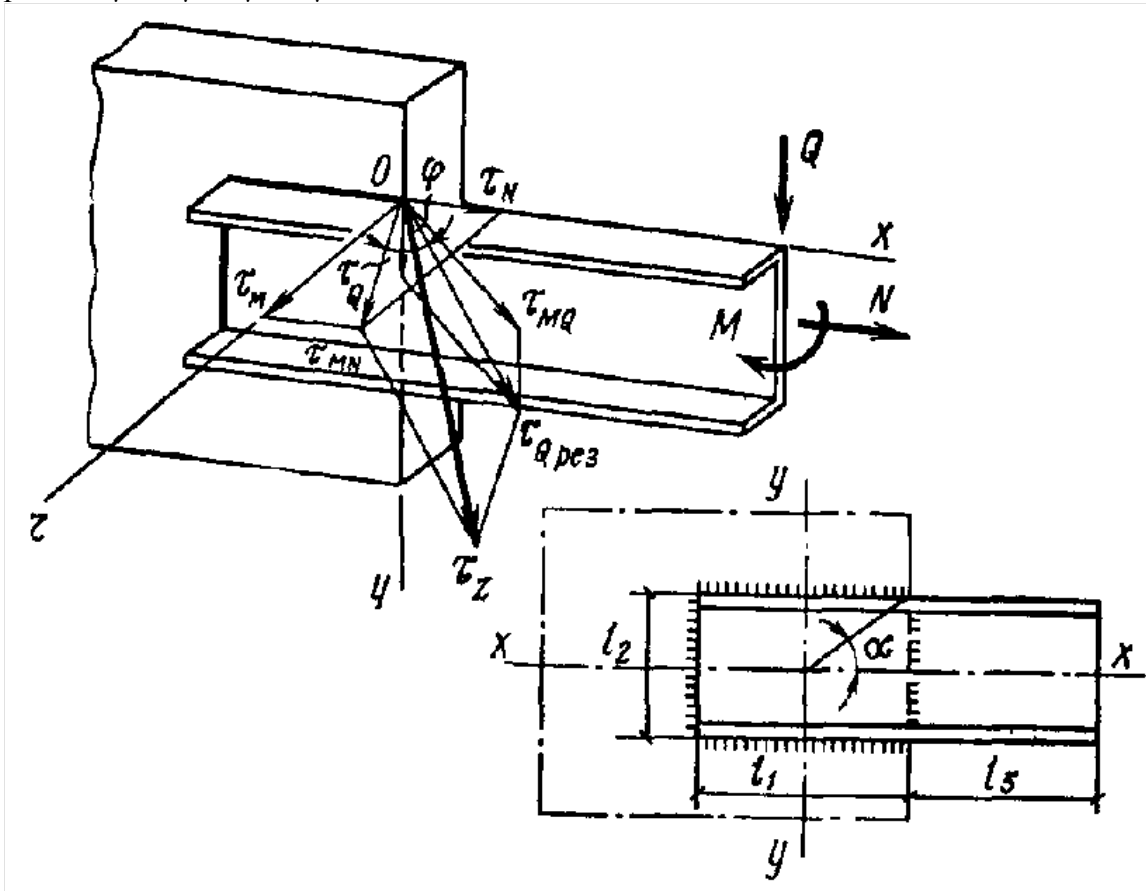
К расчету сварного соединения с угловыми швами на одновременное действие продольной и поперечной сил и момента
